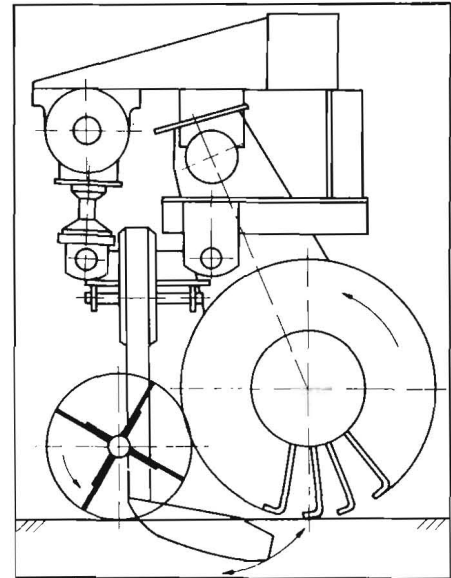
Austauschrodewerkzeuge (Plattenschare mit Förderrädern)
